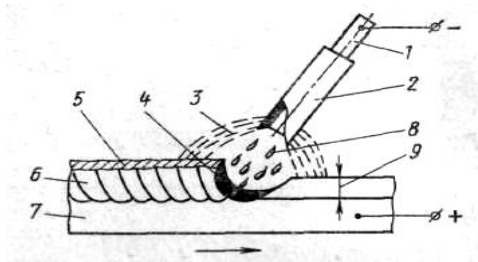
Ручная дуговая сварка металлическим электродом с покрытием:
